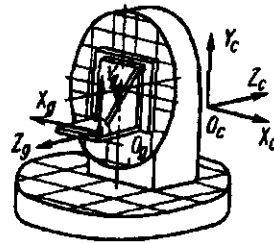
Схема расположения систем координат станка (СКС) и детали (СКД) на пятикоординатном станке с ЧПУ
